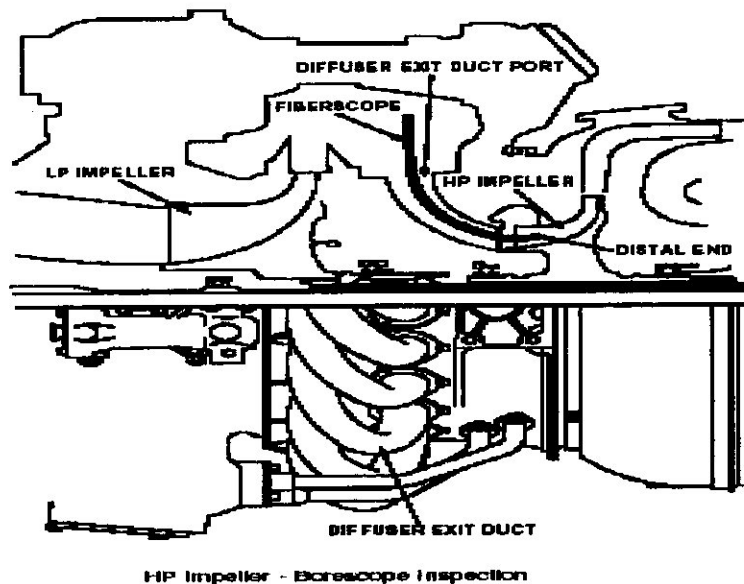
Inspection boroscopique du compresseur HP.
